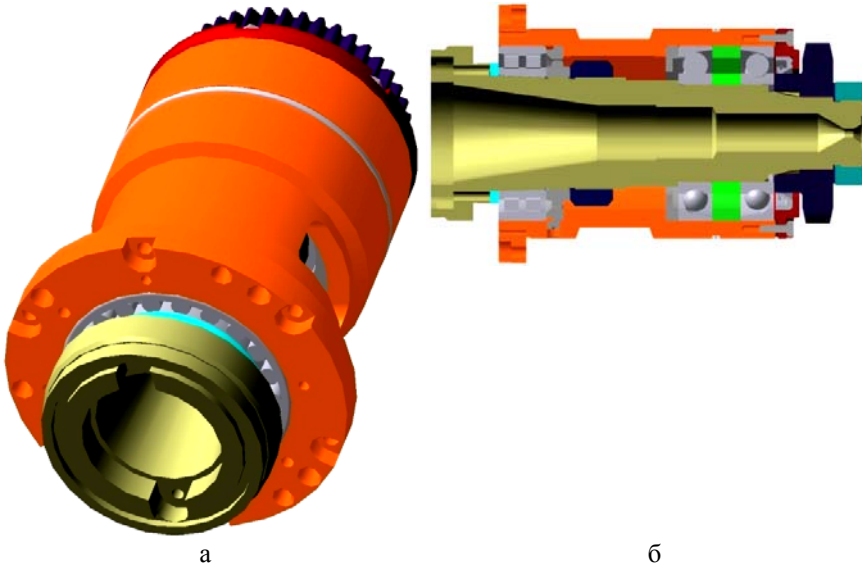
Шпиндельний вузол: а – складання; б – переріз
